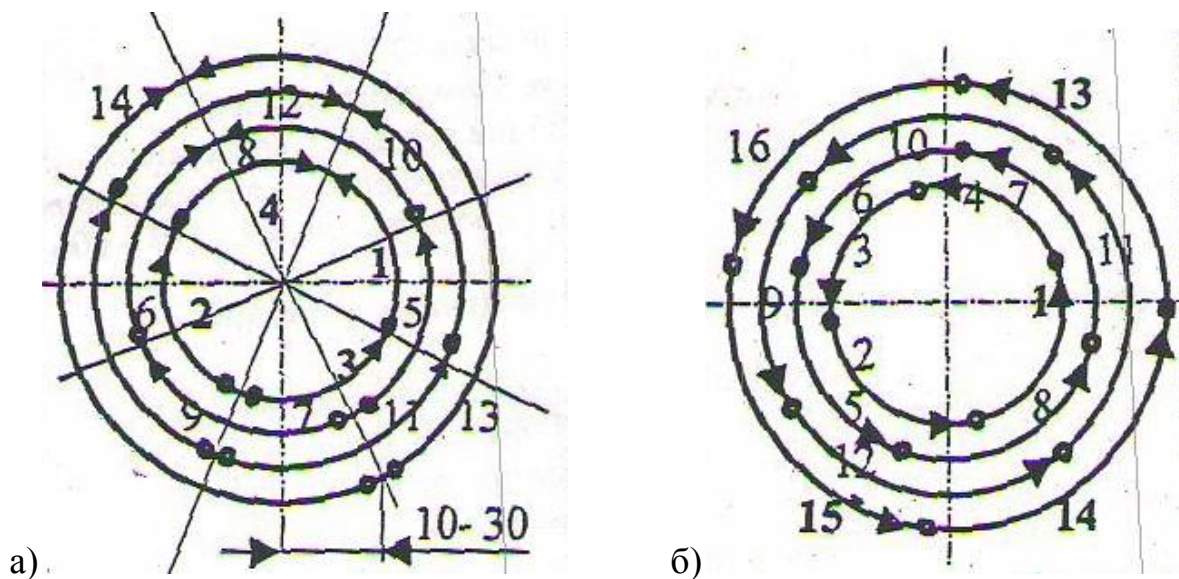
Порядок наложения слоёв при сварке стыка паропровода: вертикальный стук (а), горизонтальный стук (б)
